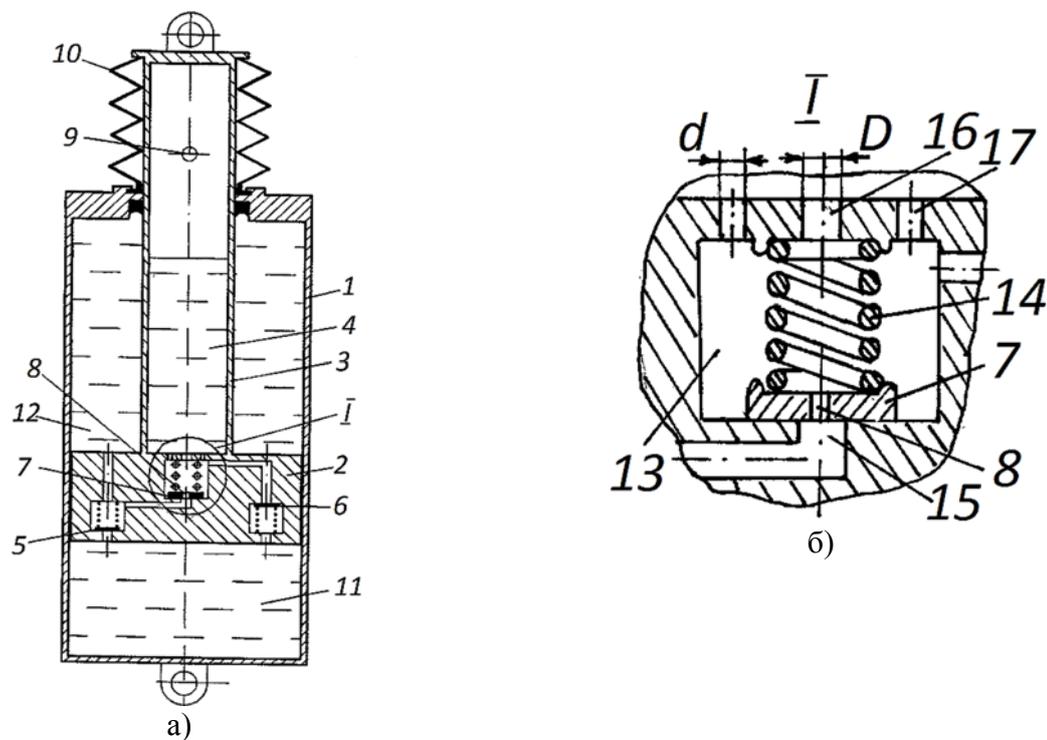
Гидравлический гаситель колебаний для транспортного средства:
